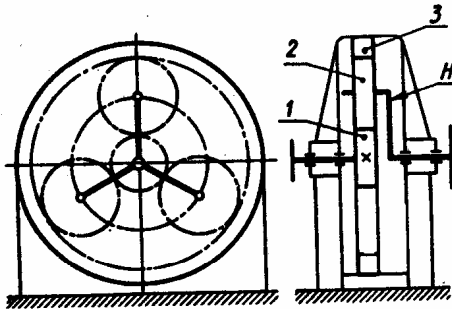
(б). Кинематическая схема планетарного одноступенчатого редуктора с ведомым водилом:
